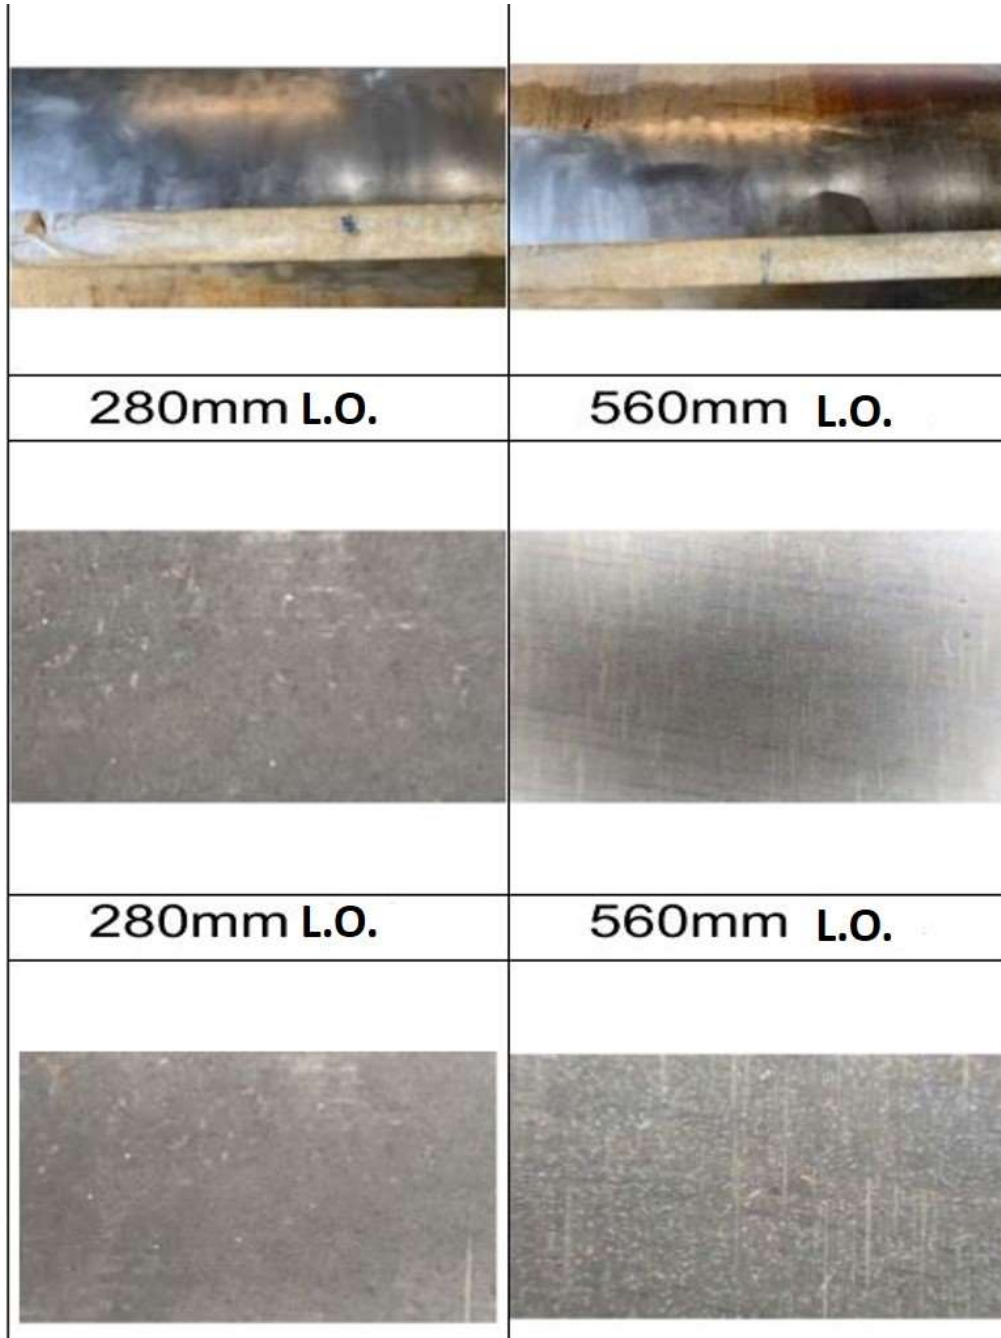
Foto em zoom lado motor. Fonte: Autor
